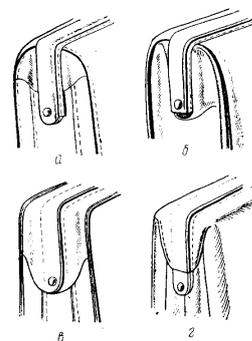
Способы соединения обтяжки с корпусом портфеля при расположении пластин внахлестку
